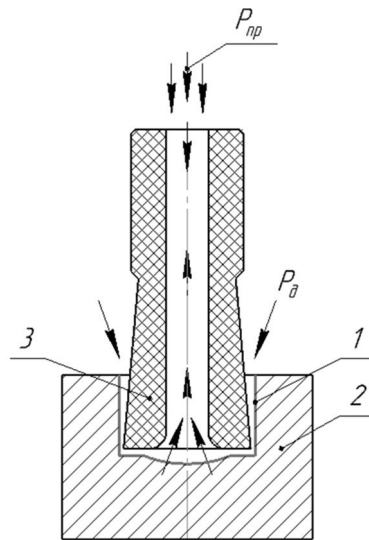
Схема формоутворення чистової обробки по внутрішньому контуру
